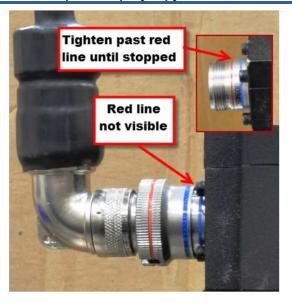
Сопряженный разъем резольвера двигателя
